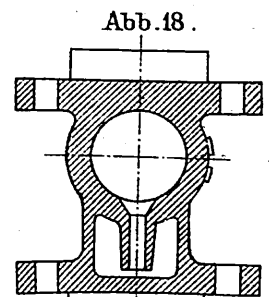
Korbuly's Zapfenlager für Eisenbahnnachsen.
